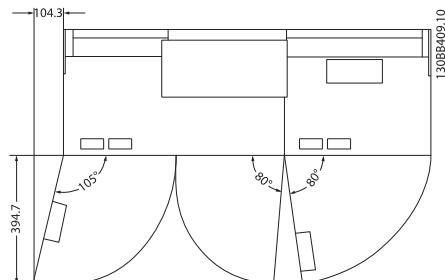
Пространство перед корпусом IP21/IP54, размер корпуса D11.
